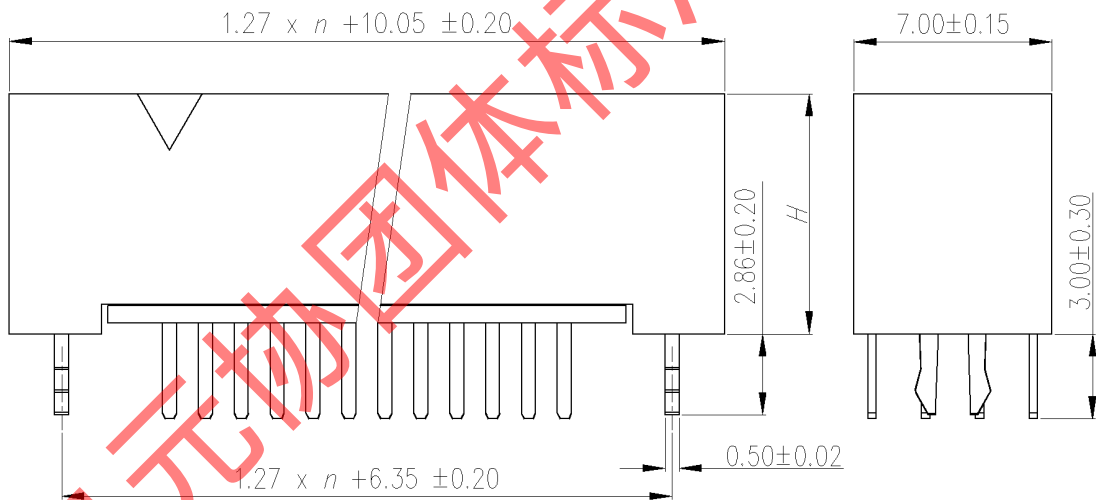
H类型插头 90度穿孔焊接式外形尺寸
